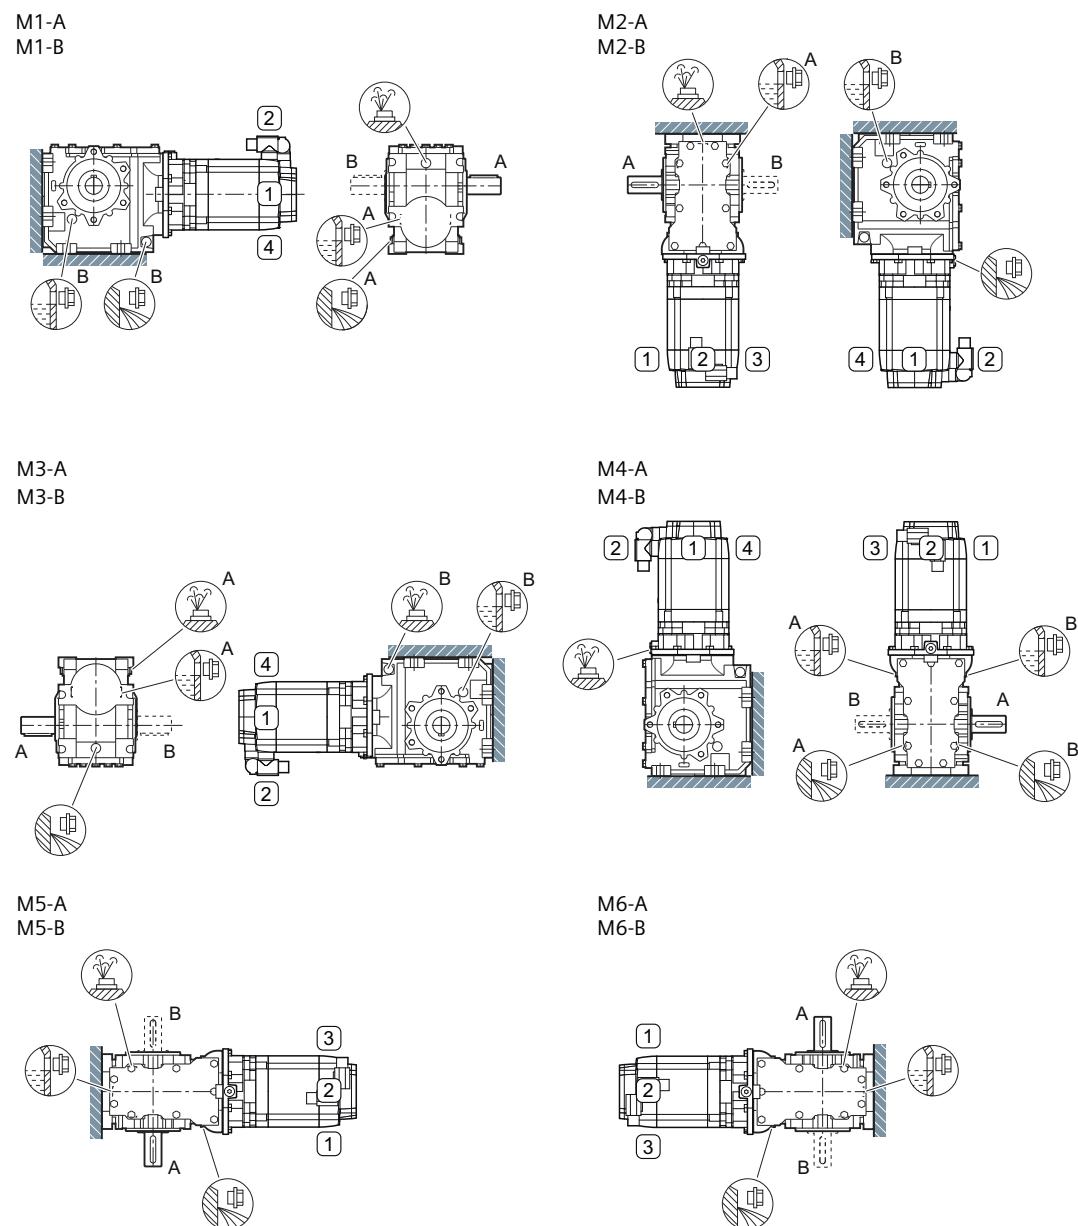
Einbaulagen für Servo-Stirnradschneckengetriebemotor C., Fußausführung, Baugröße 39A, 2-stufig
